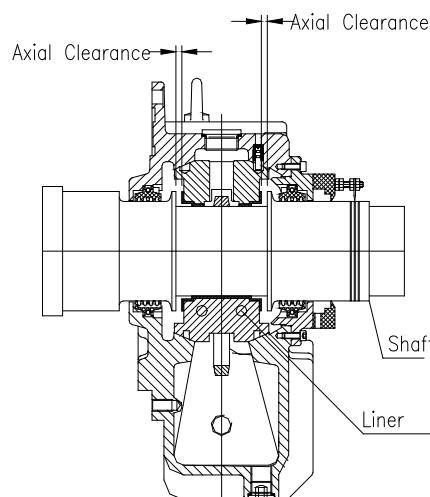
Подшипник скольжения приводного конца вала
